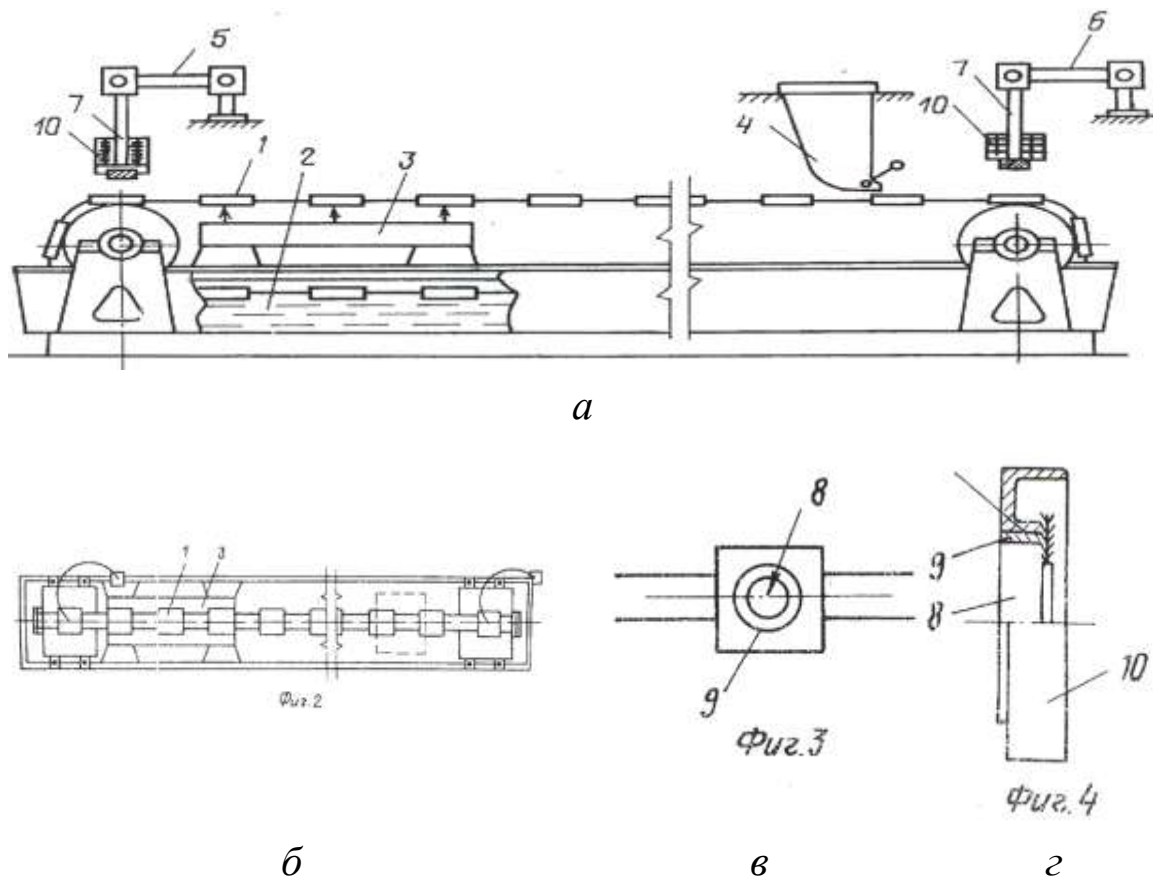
Принципиальная схема устройства для выпечки полуфабриката из теста: а – общий вид; б – устройство (вид сверху); в – отдельный элемент формы; г – разрез
